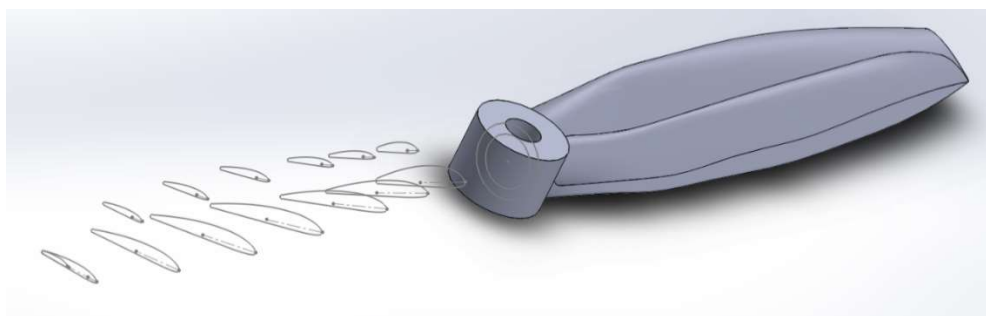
Пространственный 3D-вид билопастного воздушного винта
